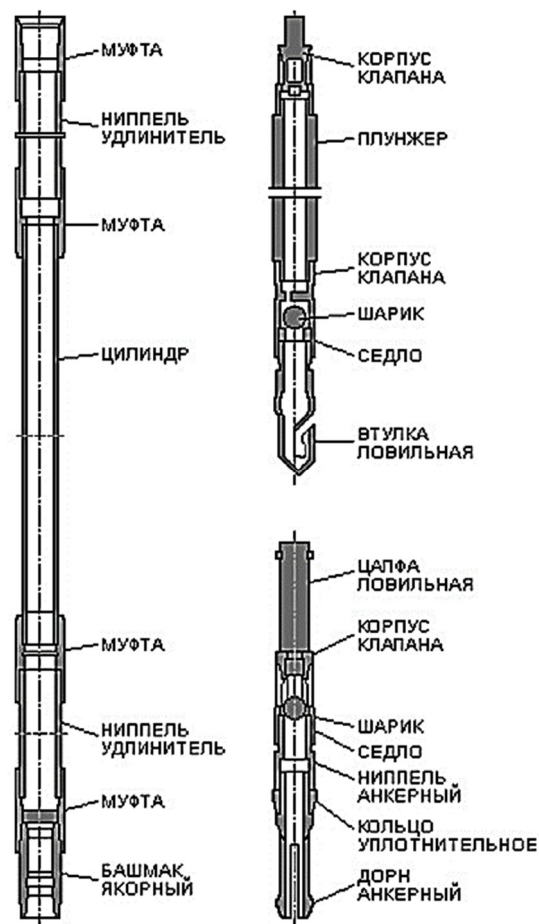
Насос ГШН трубный со стандартным (по 11АХ-АРІ) креплением всасывающего клапана
